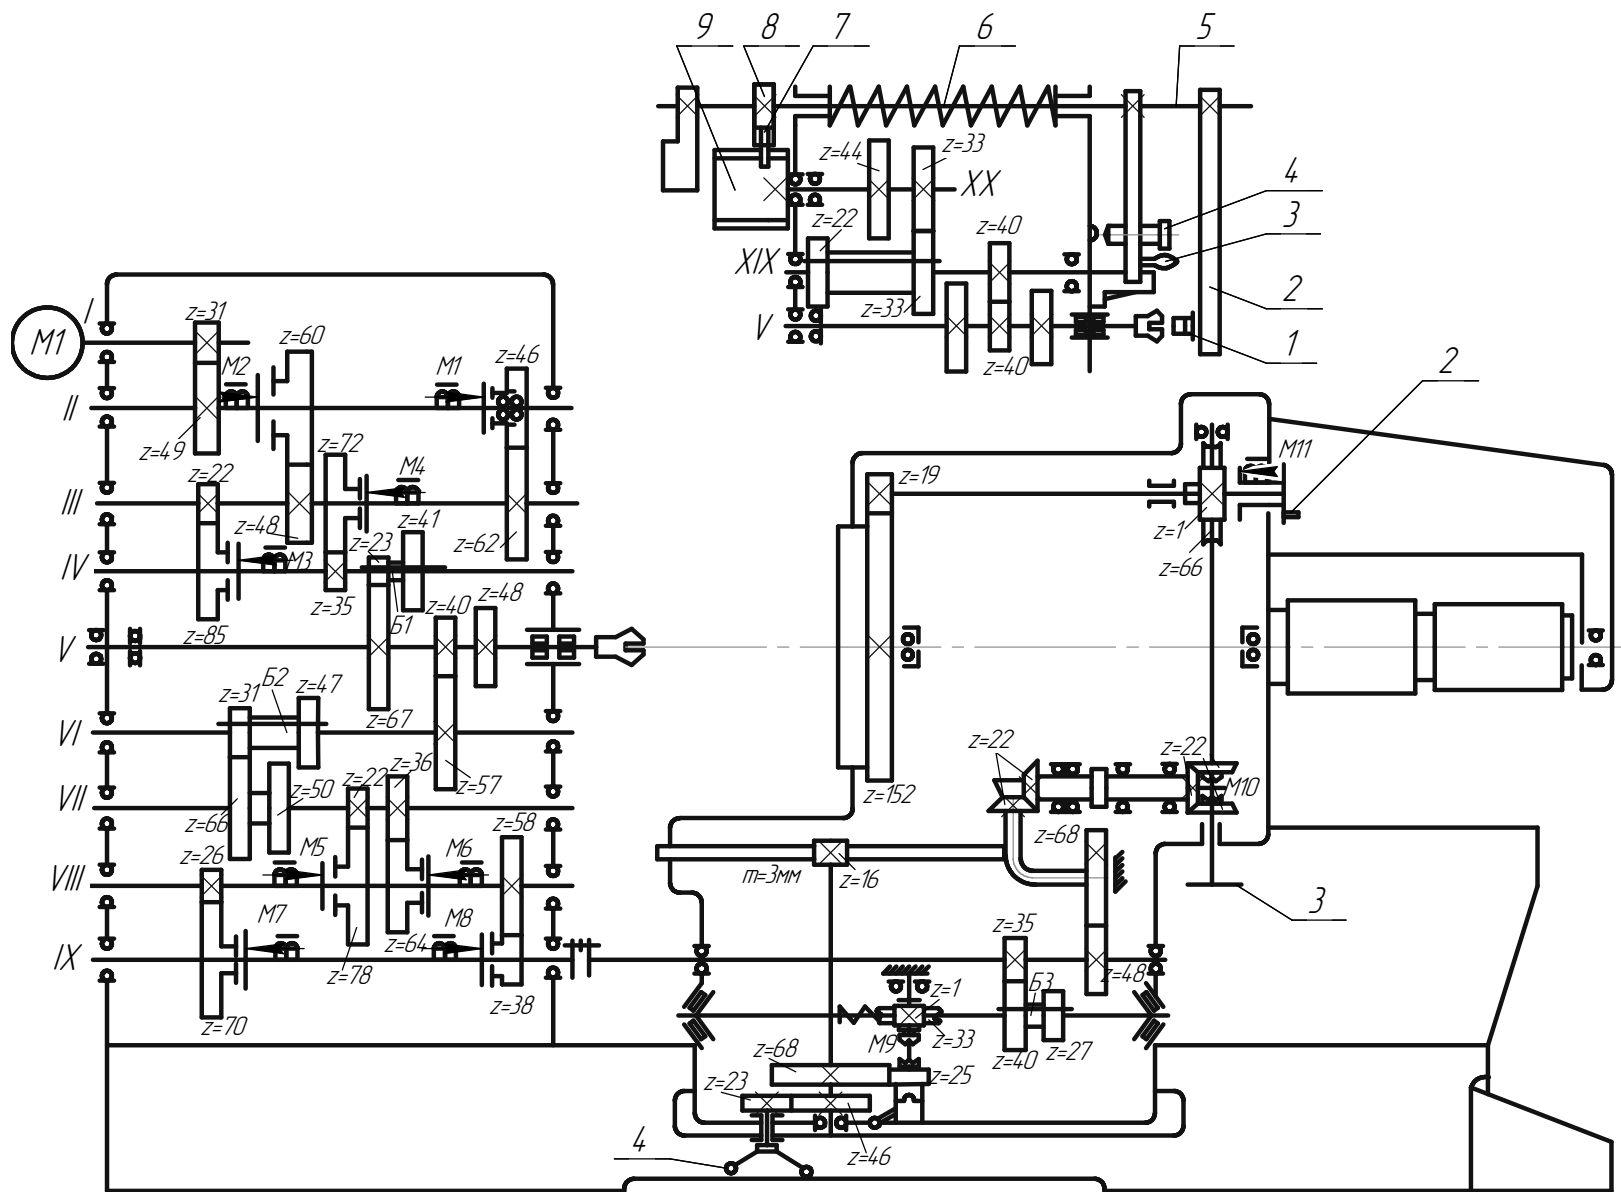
Кінематична схема токарно-револьверного верстата моделі 1341
